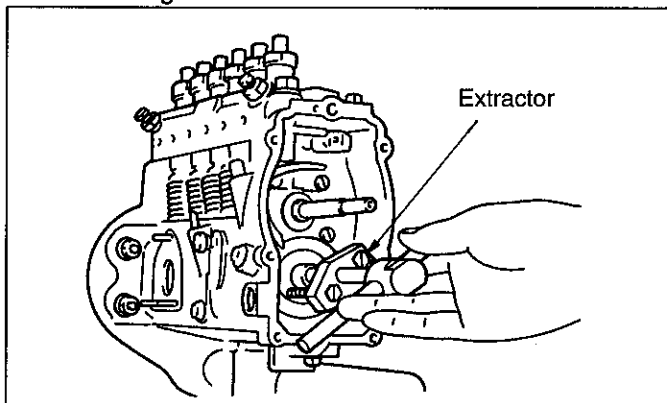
Desmontaje del conjunto de engranaje del regulador
